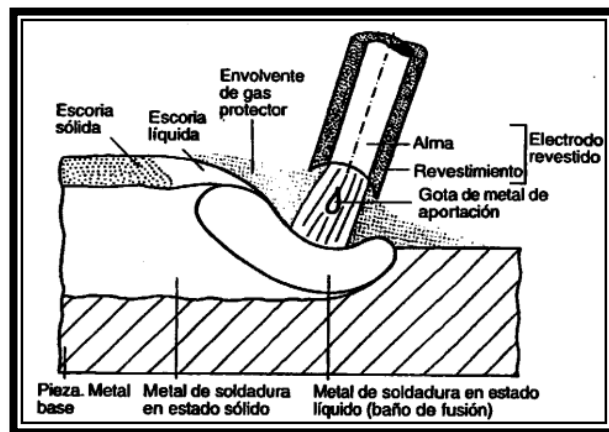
Elementos de la Soldadura SMAW.
